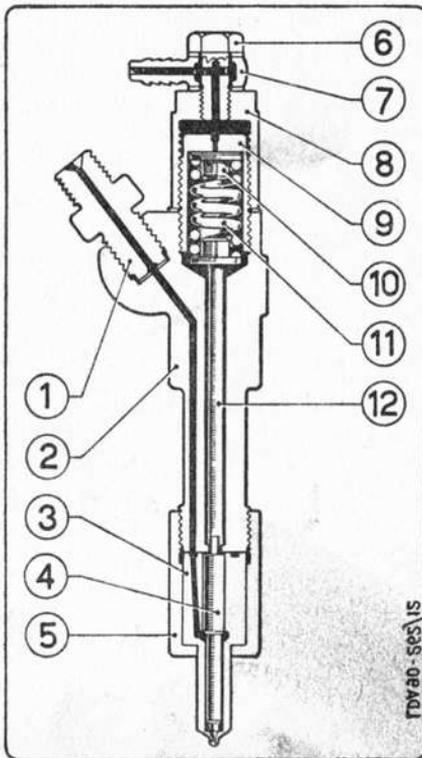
SCHNITT DURCH DEN BRENNSTOFF - DÜSE MIT DEN DÜSENHALTER.
